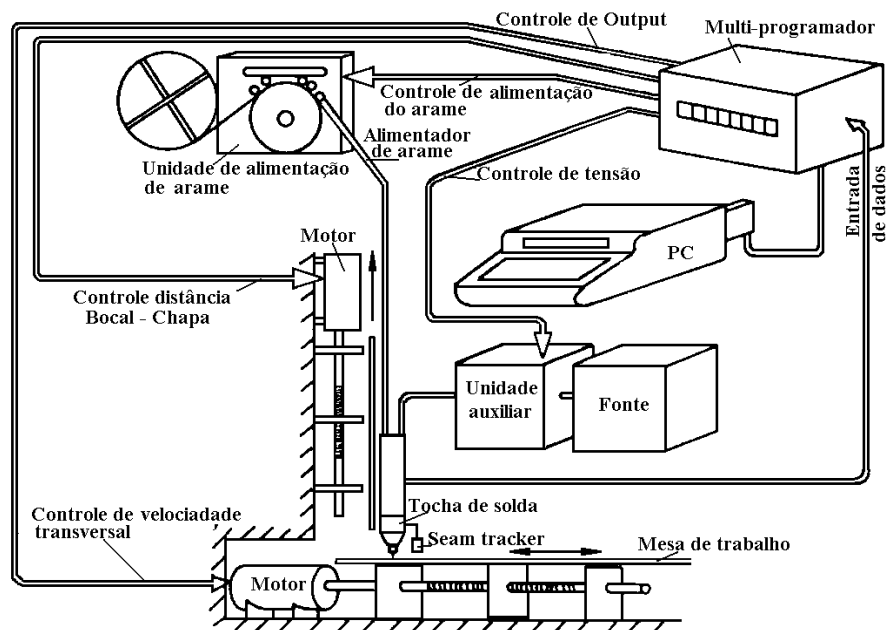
diagrama esquemático para um sistema de soldagem automatizado.
